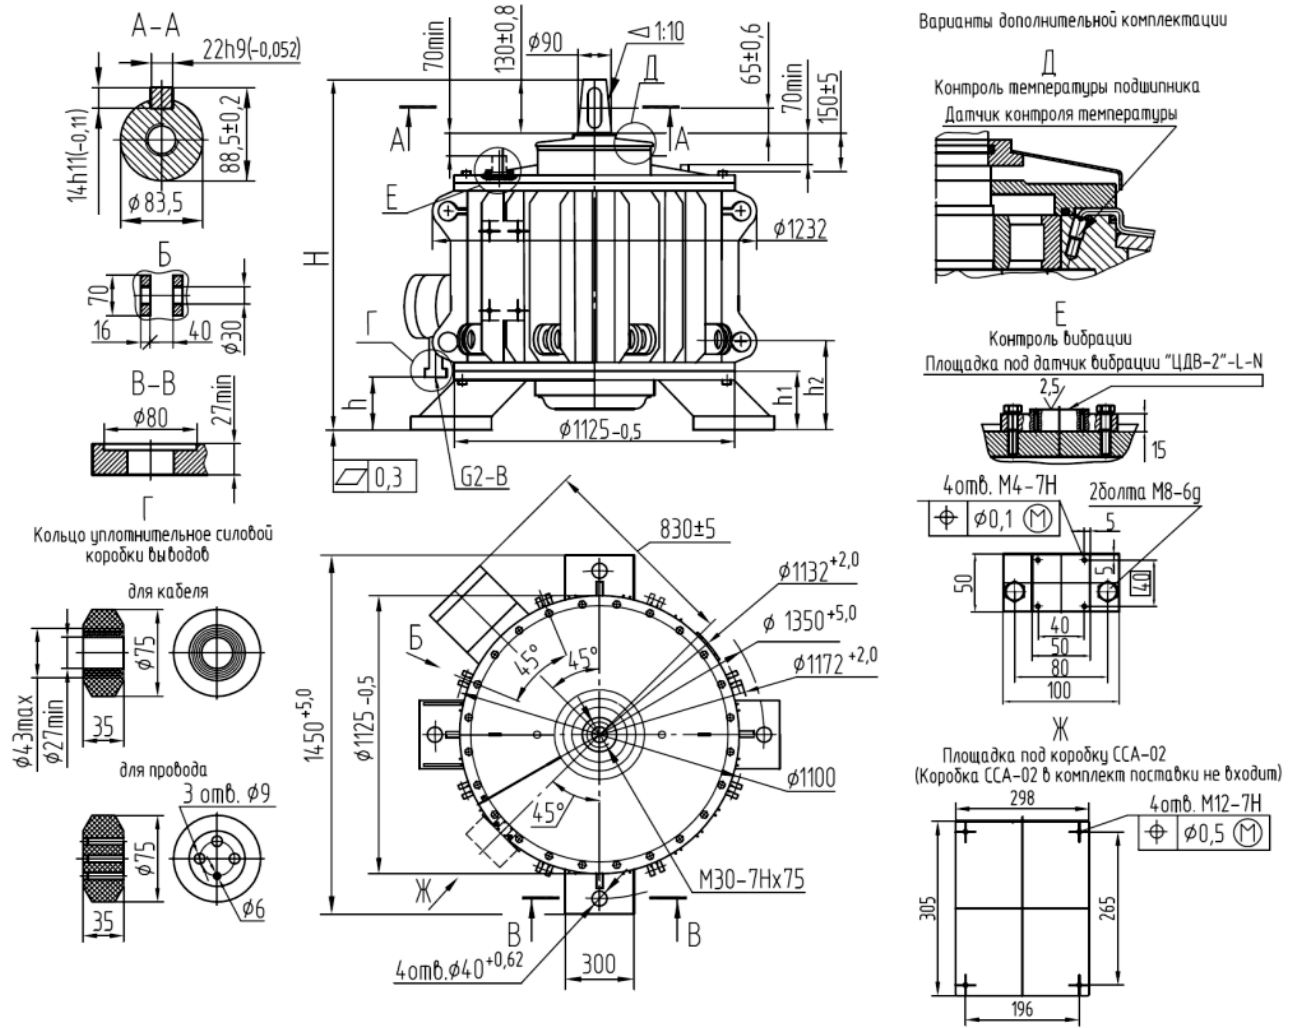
Габаритные и присоединительные размеры двигателей ВАСО5К
